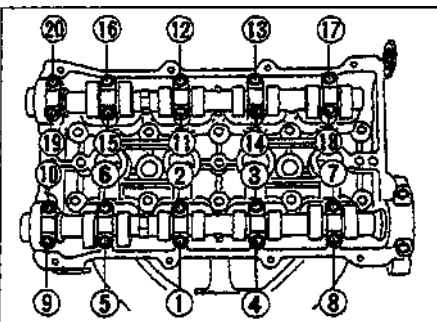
, б. Порядок затяжки болтов крышек опор распределительных валов [двигатель 1.8 литра с двумя распределительными валами]
